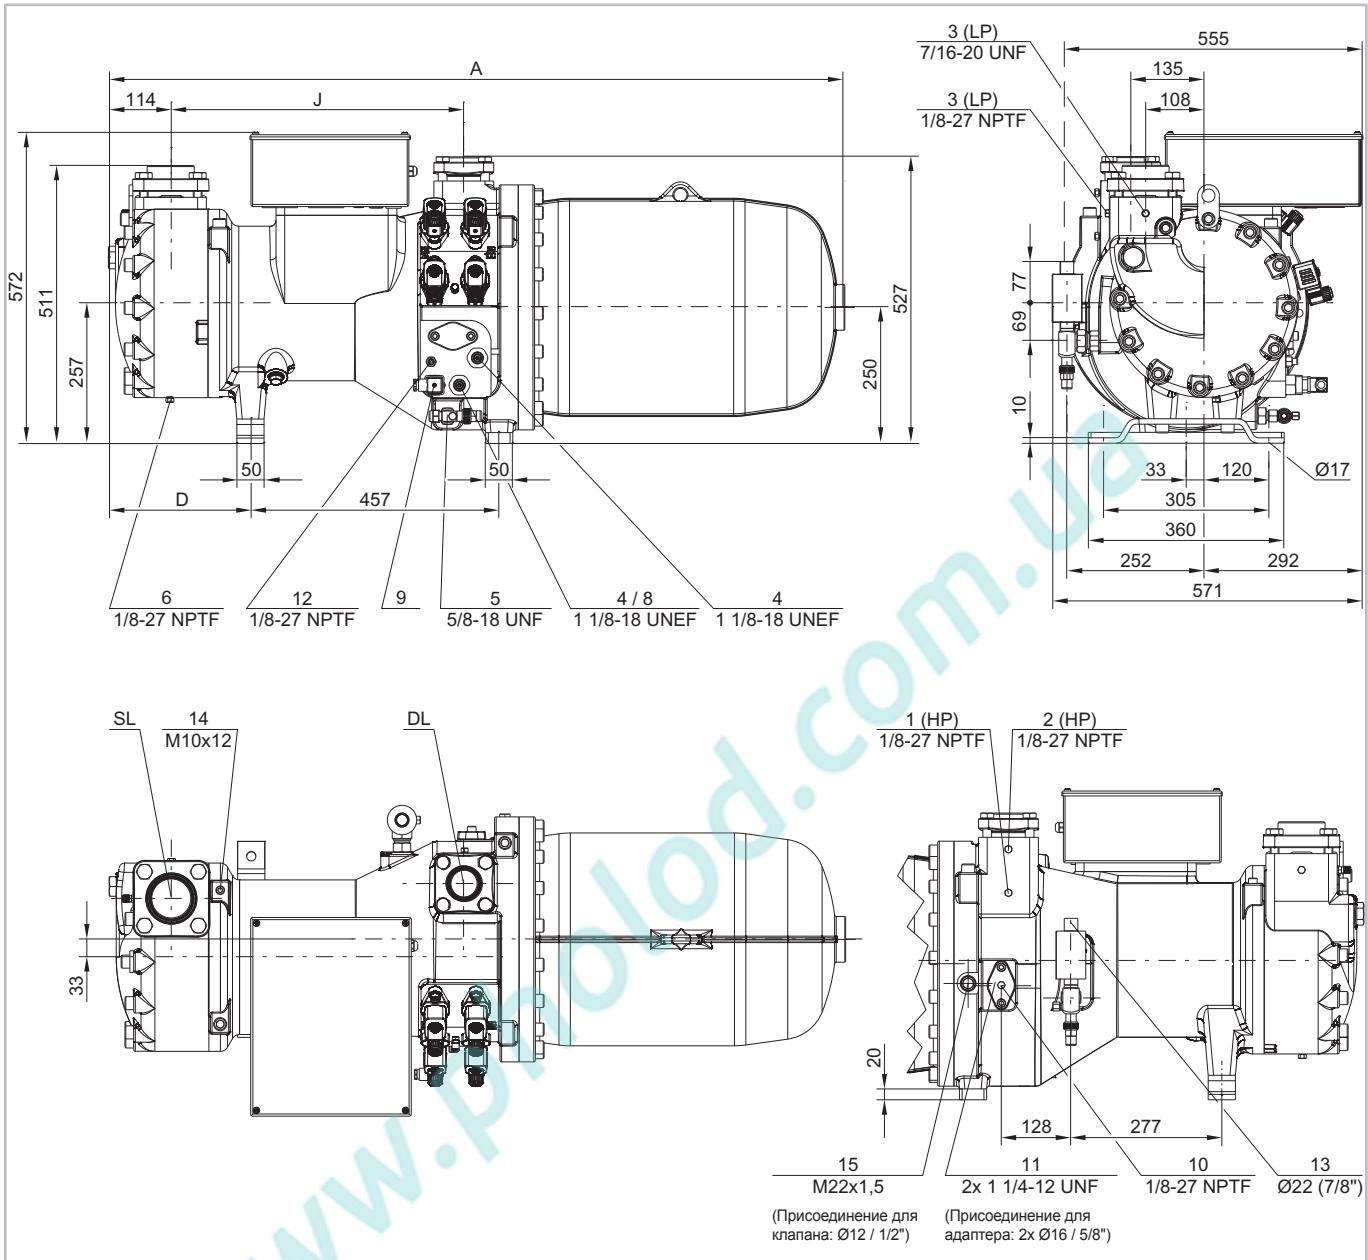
Чертежи с указанием размеров для компрессоров CSH7553-50Y .. CSH7593-110(Y)
